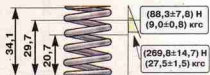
Основные данные для проверки внутренней пружины клапана
